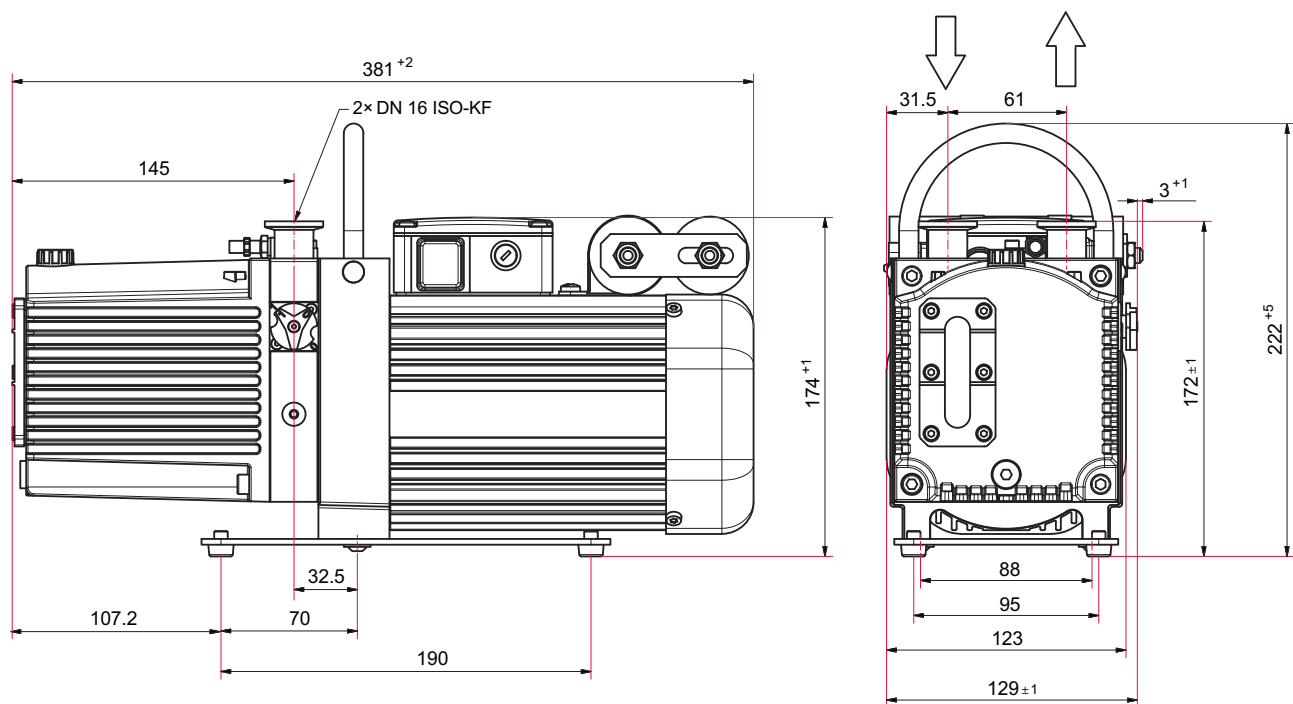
Dimensões do Duo 6, motor monofásico, 115/230 V, 50/60 Hz
